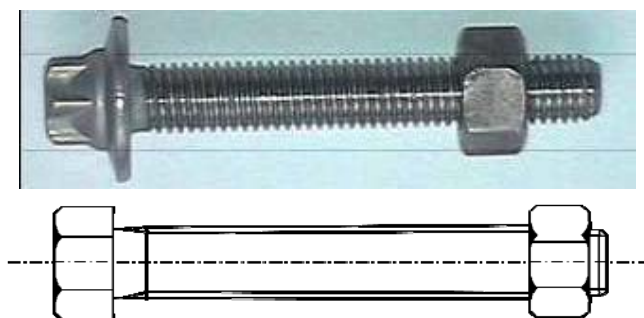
EN AW-6056-T6, Schraube mit metrischem Gewinde M10x90 gemäß DIN 13-1 [DIN8] $K_t=4,7$ [Wut07], $K_t=5,1$ [Schn10-2]
